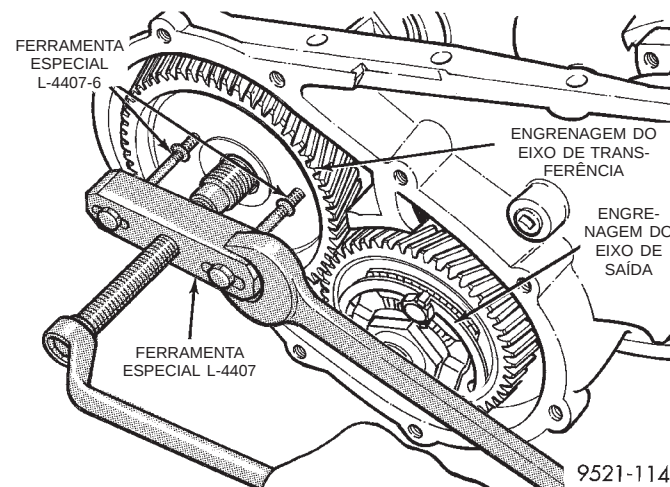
Remoção da Engrenagem do Eixo de Transferência
